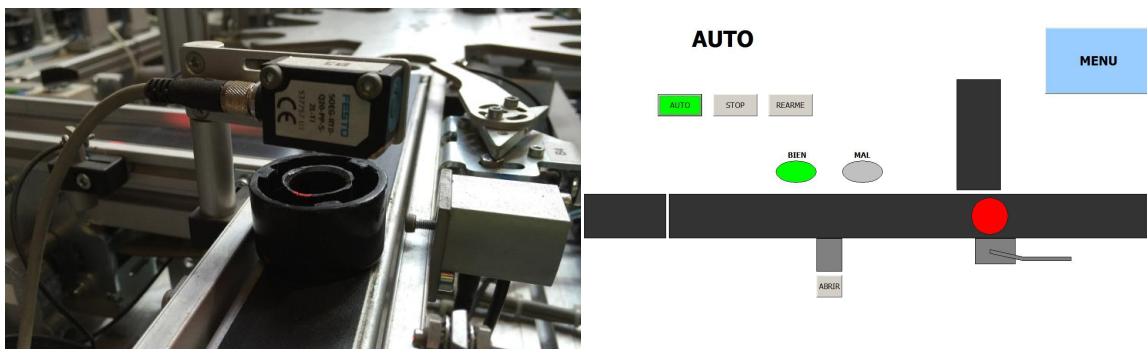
Posición 1 (pieza ok) del modo automático de separación.
